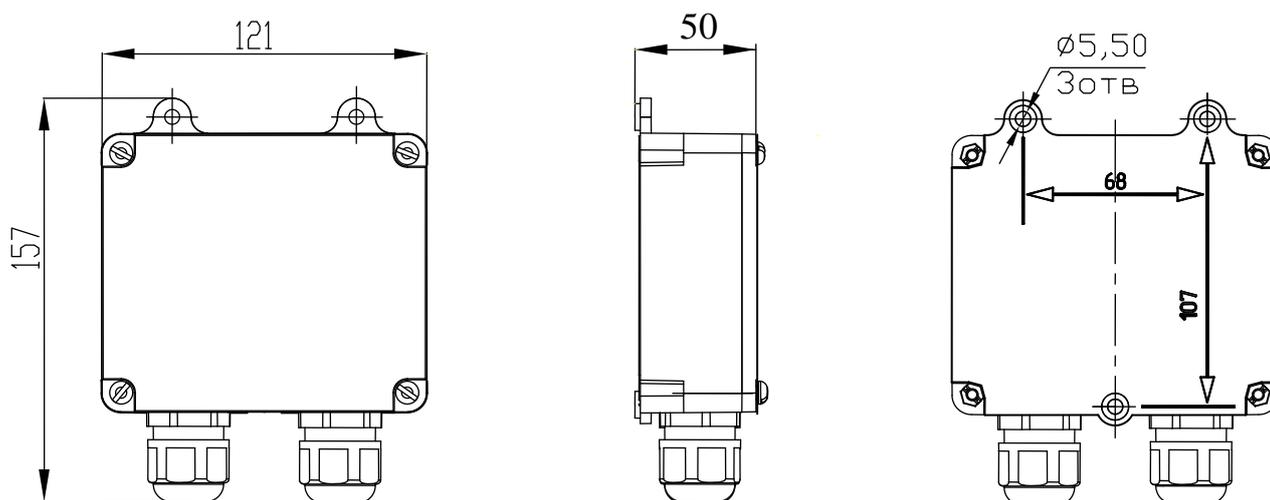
Габаритные и установочные размеры оповещателя ОС-12/В «АЯКС»
